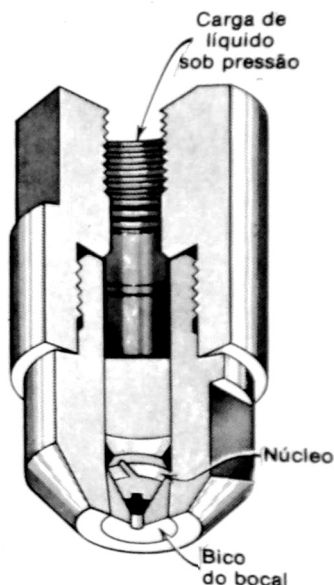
Vista em corte da secção longitudinal de bocal a pressão
